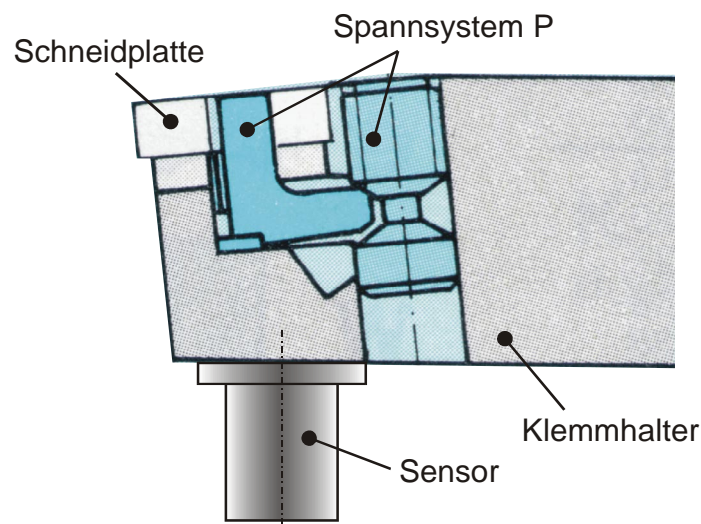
Sensorposition für Referenzmessungen am Drehwerkzeug
